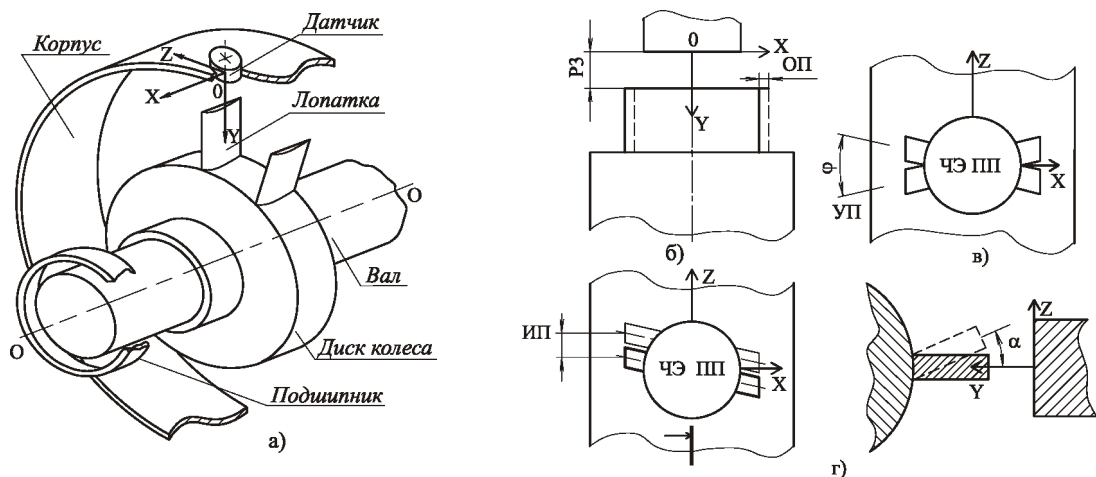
Элементы ротора лопаточной энергетической установки (а) и развёртка лопаточного венца с линейными (б) и угловыми (в, г) перемещениями лопаток
